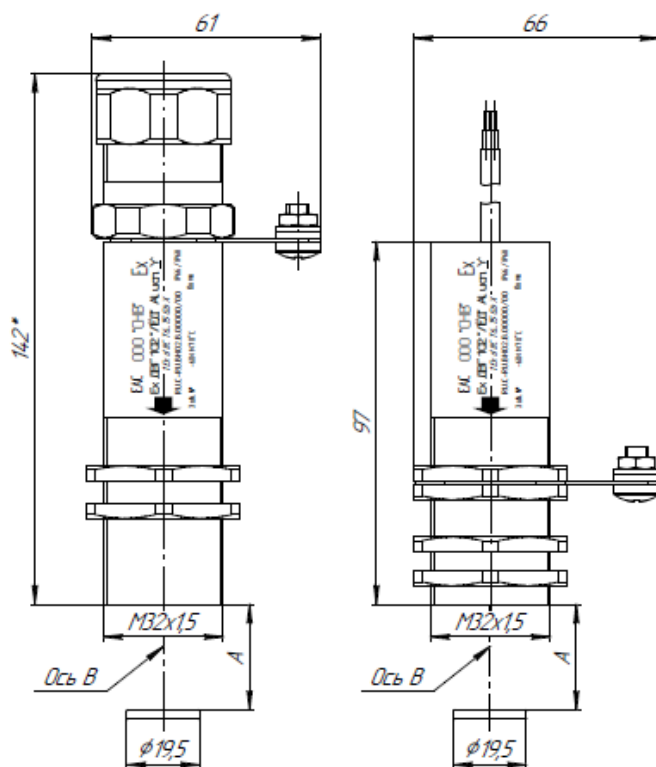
конструкция датчиков Ex ДВГ 102 «ЛЁД» с торцевой рабочей зоной, постоянно присоединенным кабелем или кабельным вводом и резьбовым креплением к поверхности.
